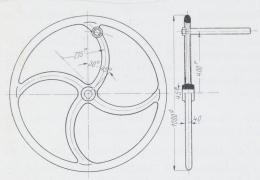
Schwungrad für von Hand betriebene Maschinen. M. 1:20.
